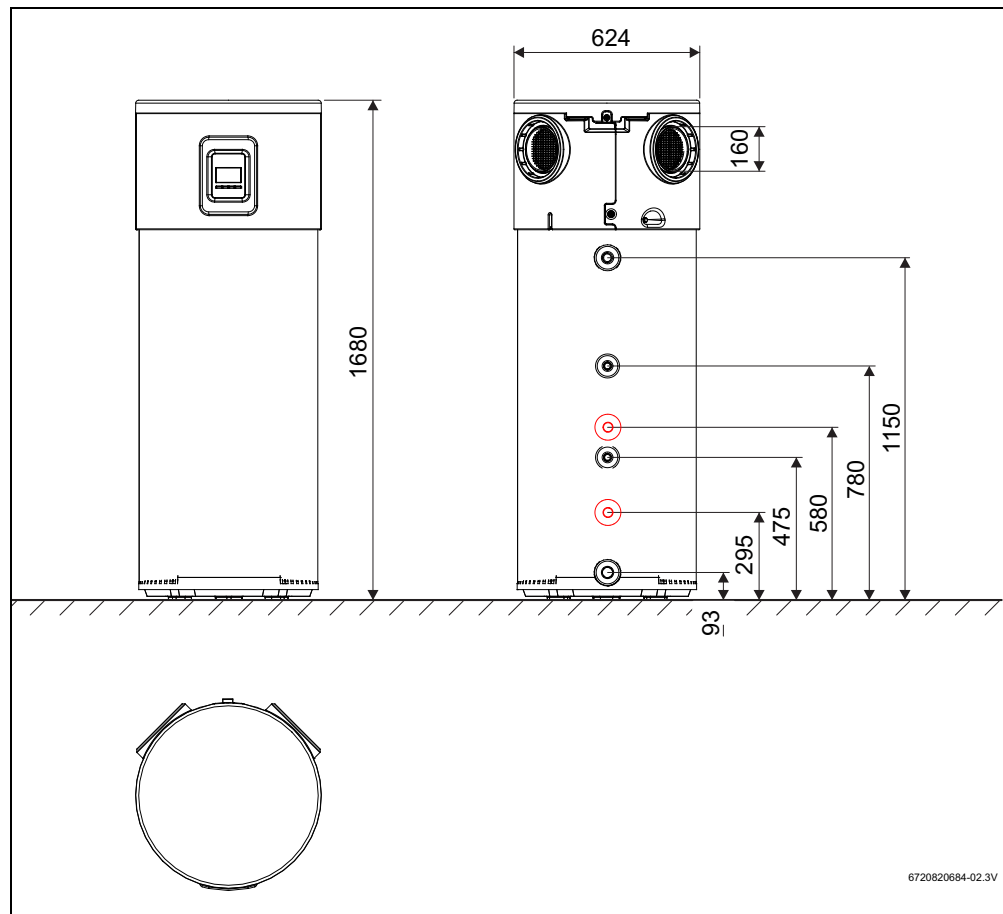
Dimensiones del aparato de 200 l (en mm)
